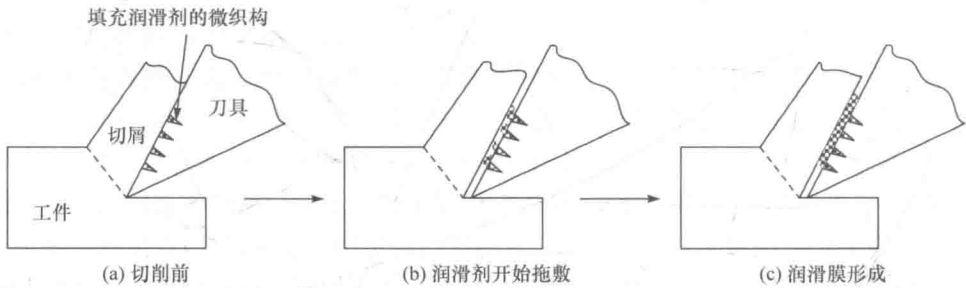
微织构刀具切削加工时形成润滑膜示意图
